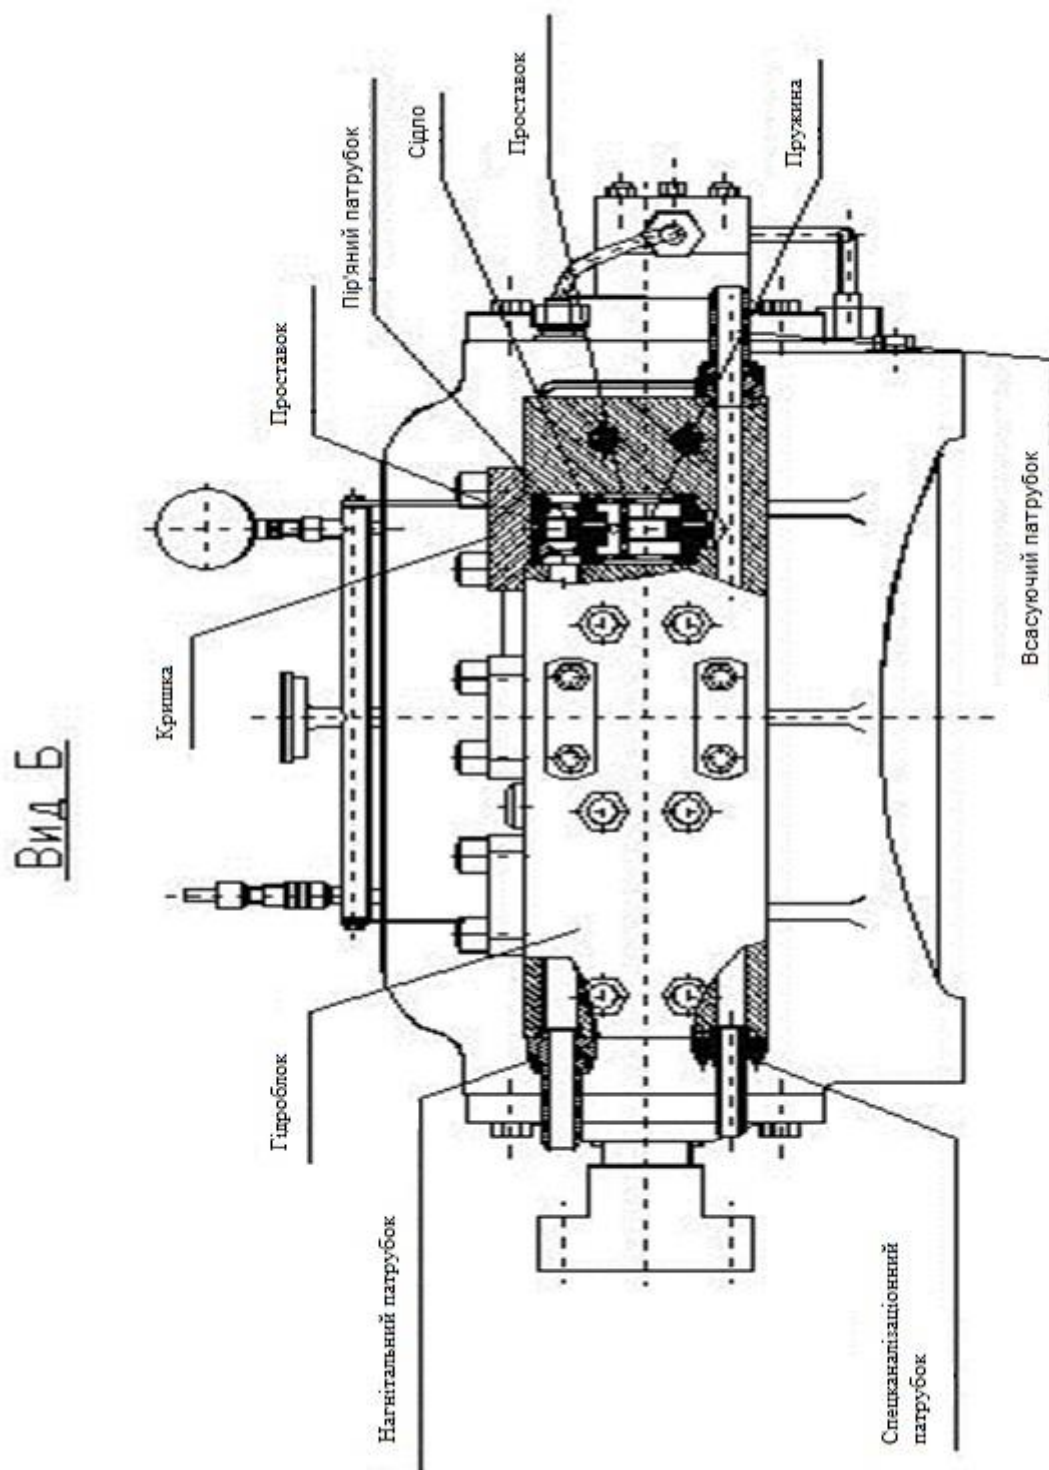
Креслення насоса ПТ6 / 160-С- вид Б [122]
